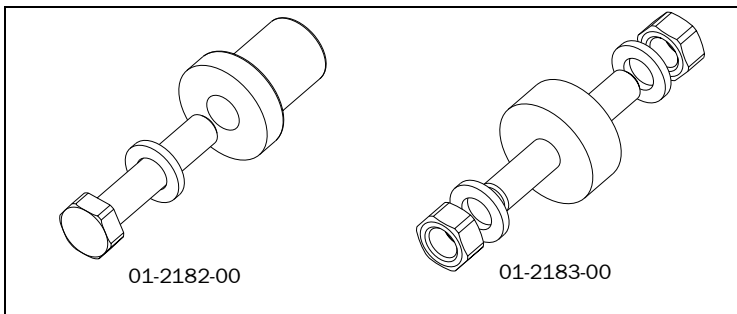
Montagesätze mit Schwingungsdämpfung für den Motor
